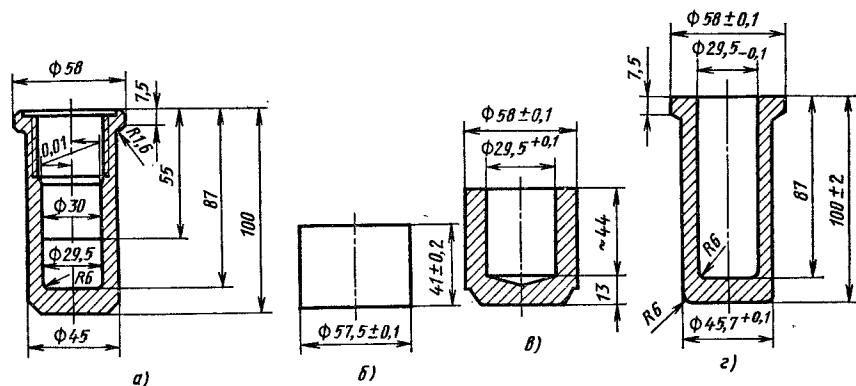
Корпус гидравлического сосуда и переходы штамповки:
